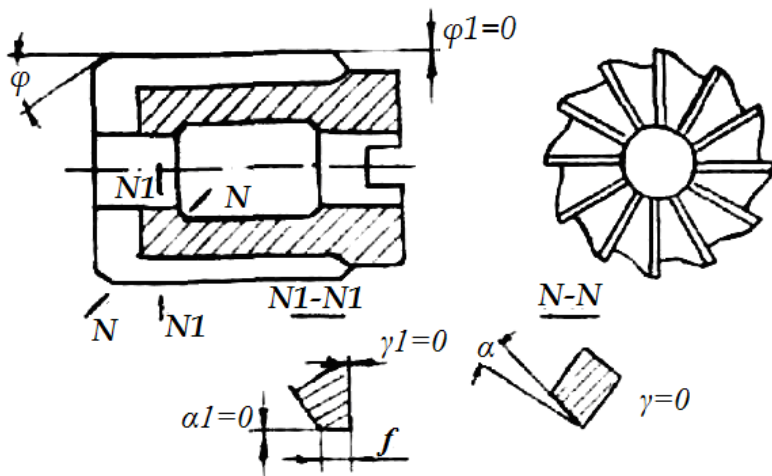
Насадна циліндрична розвертка для обробки глухих отворів
